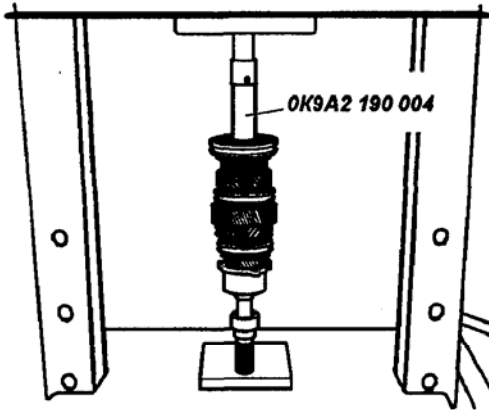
Установка ступицы и муфты синхронизатора 3 и 4 передач
